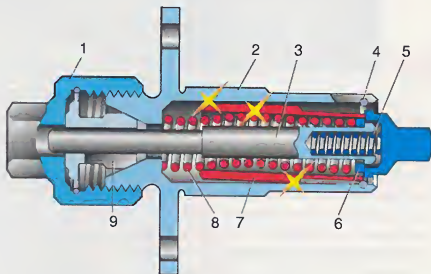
Натяжитель цепи: 1 — колпачковая гайка; 2 — корпус; 3 — стержень; 4 — стопорное кольцо; 5, 8 — пружины; 6 — шайба; 7 — плунжер; 9 — цапговый зажим (сухарь).
